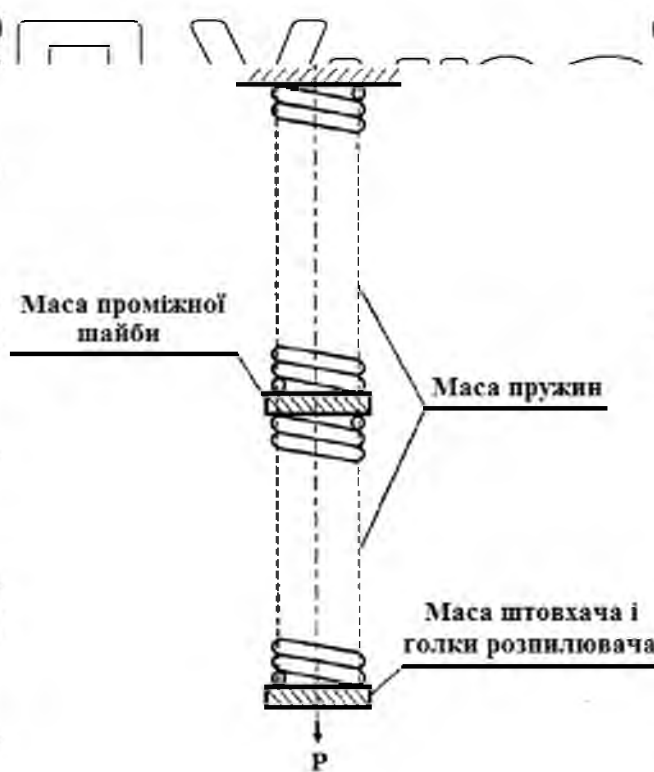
Розрахункова схема насадки з композиційною пружиною
